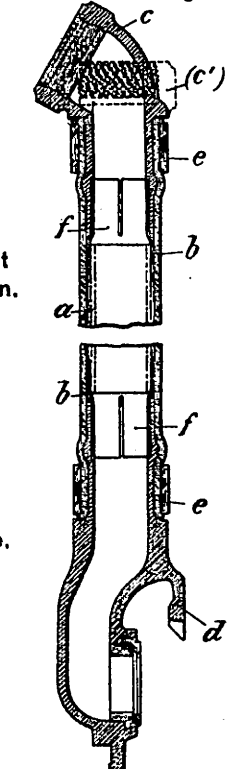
Geschweißter Schlauch aus mehrweiligen Rohrstücken.
